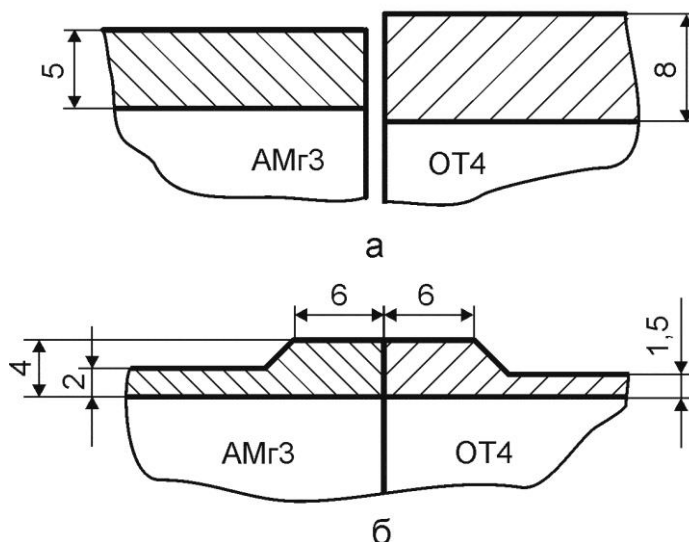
Толщина стенок в зоне стыка трубных заготовок (а) и переходника (б)
